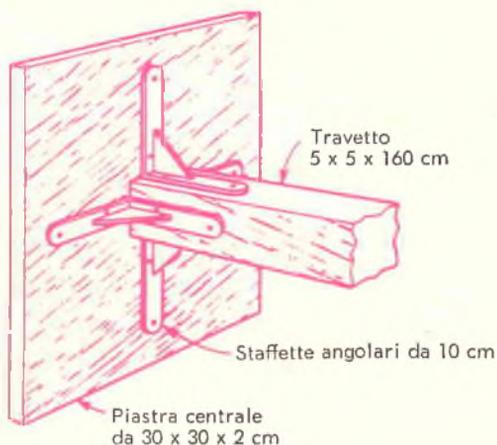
La parte più critica dell'antenna è costituita dalle giunzioni delle piastre centrali al travetto di unione. Prima di installare l'antenna assicuratevi quindi che le piastre siano fissate saldamente.
